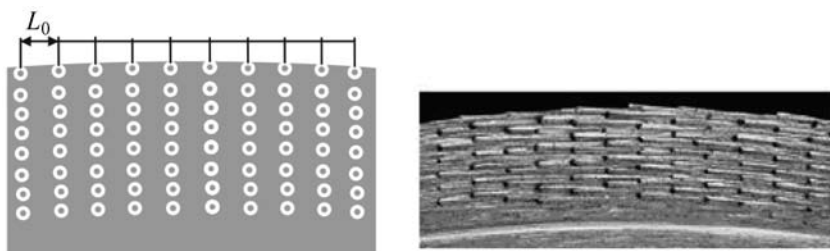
Схема расположения зерен алмаза и внешний вид рабочей поверхности шлифовального круга, изготовленного по технологии ARIX
